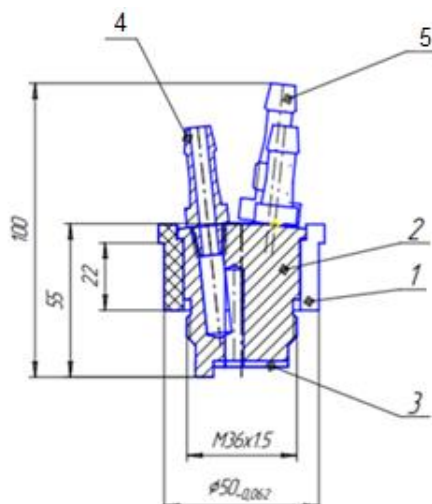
Хвостовик плазмотрона, где 1- втулка изоляционная, 2-корпус, 3-прокладка резиновая, 4- ниппель, 5- штуцер.
